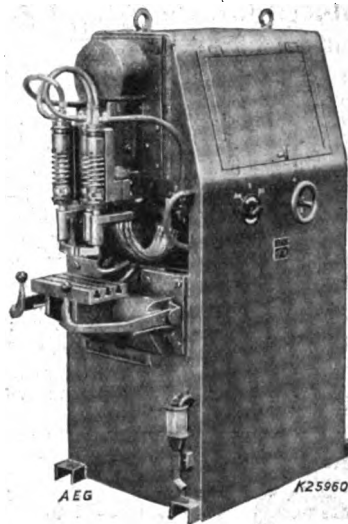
Mehrfach-Punktschweißmaschine.
